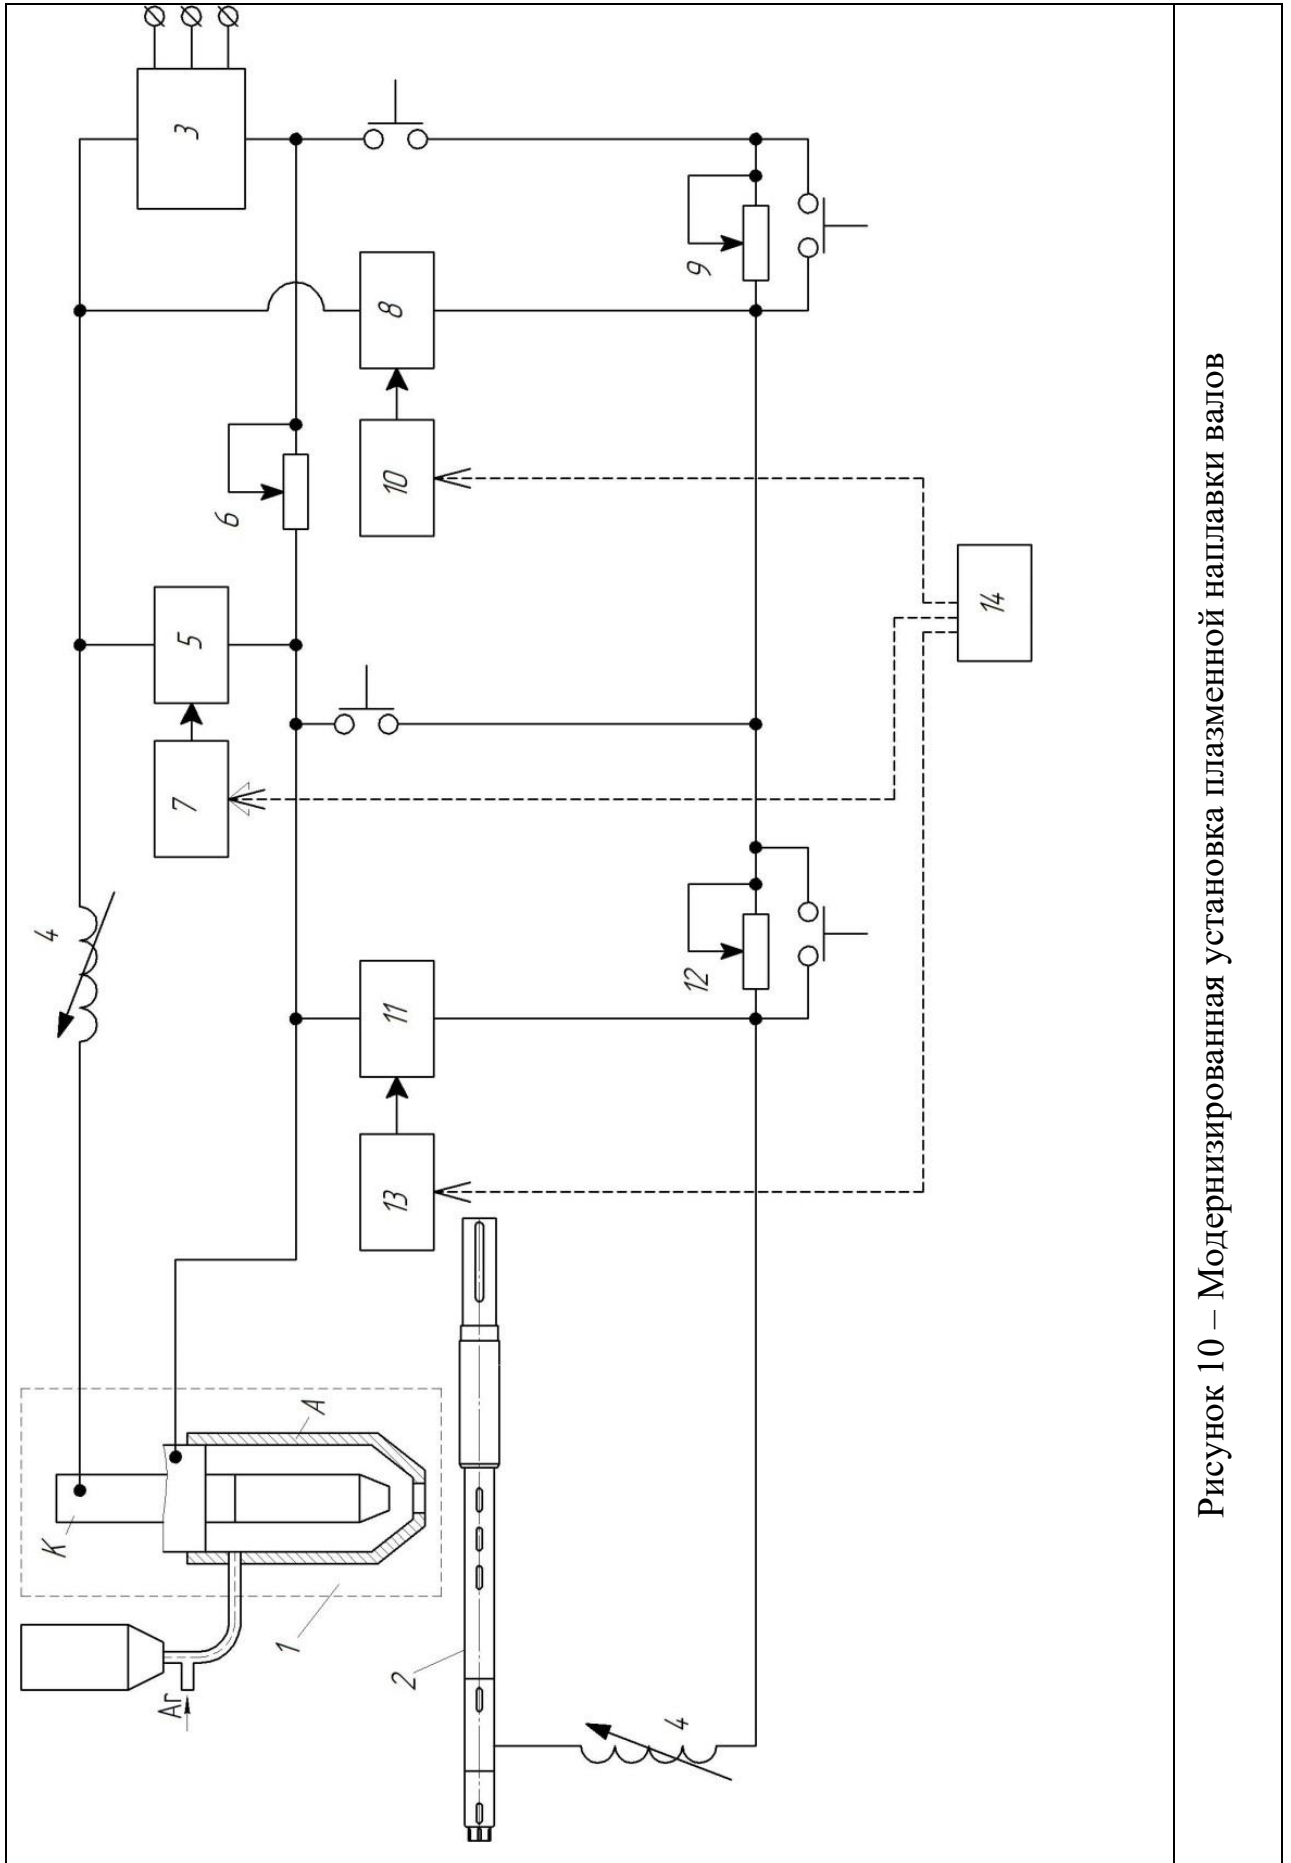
Модернизированная установка плазменной наплавки валов
